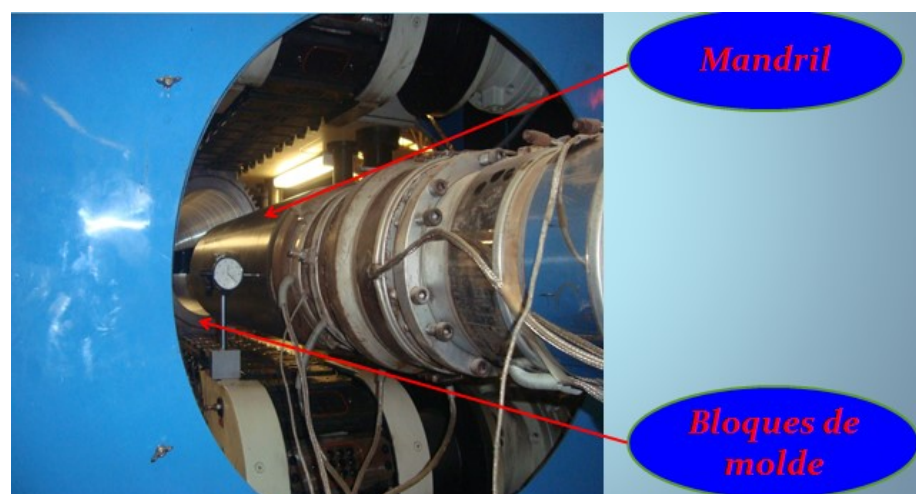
Bancada superior e inferior, bloques de molde, mandril.
